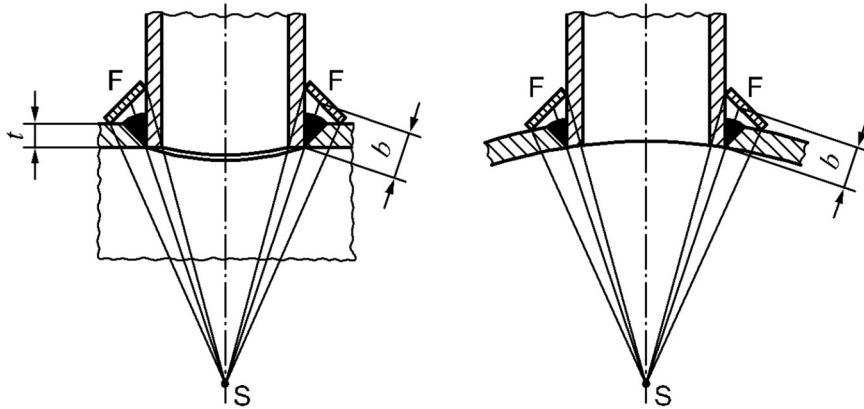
Схема контроля сварных швов вставных деталей с источником излучения, расположенным на центральной оси трубы, перпендикулярно центру сварного шва, и пленкой снаружи
